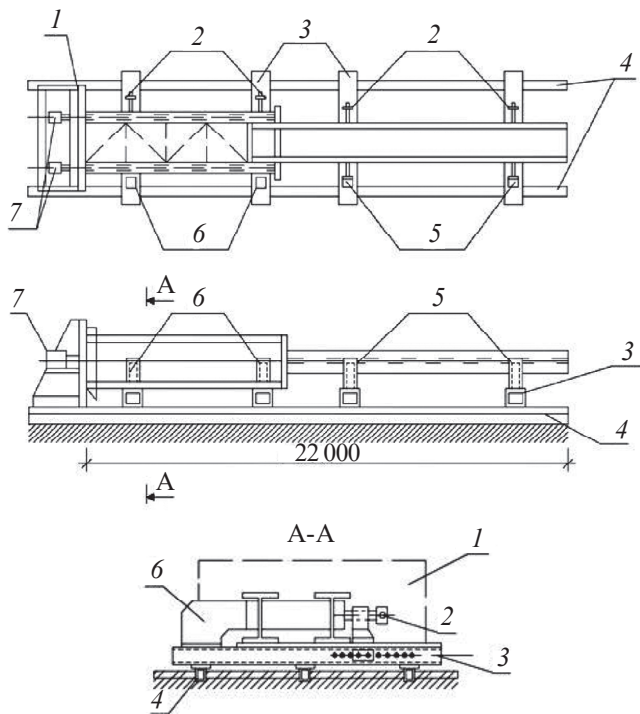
Кондуктор для сборки решетчатых колонн:
